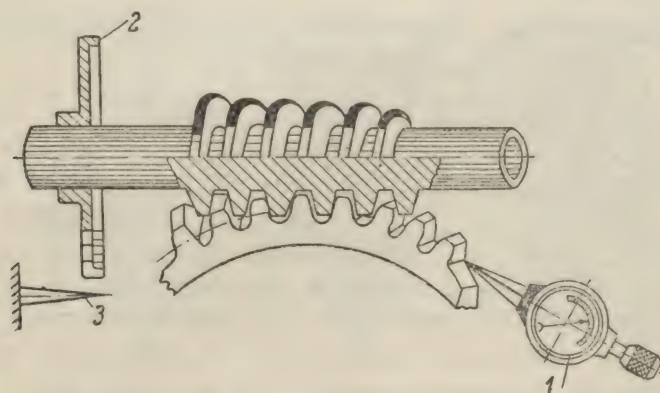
Схема проверки бокового зазора в червячных передачах.
